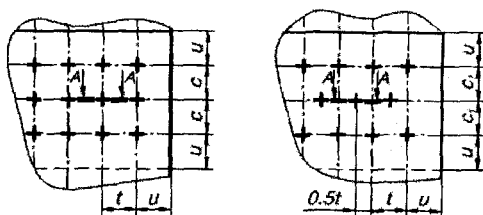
Конструктивные элементы сварных соединений, выполненных контактной точечной сваркой
